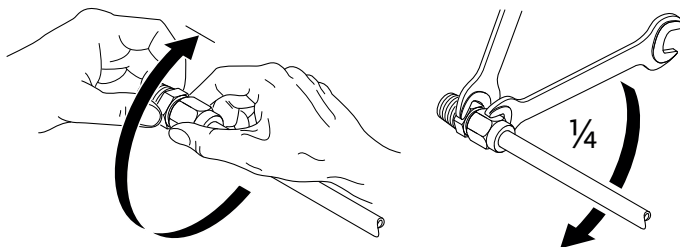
1/4 de rotação adicional da abraçadeira de ligação
